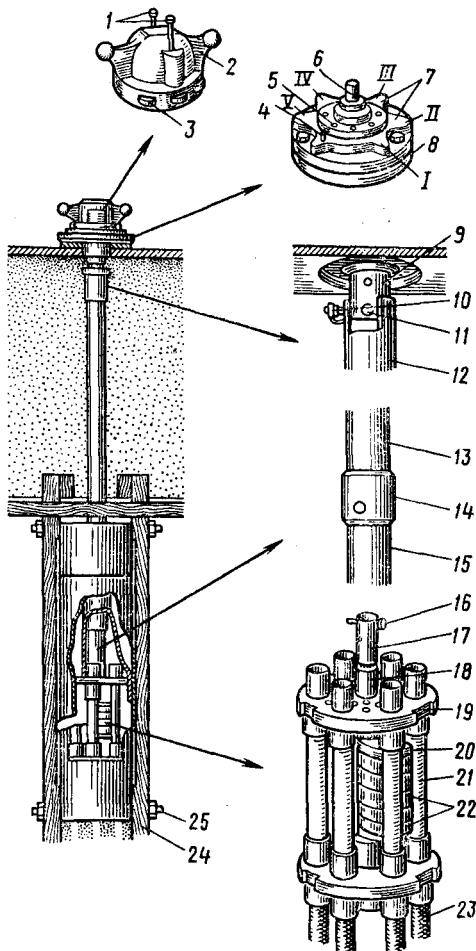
Общий вид и детали однофазного переключателя барабанного типа:
